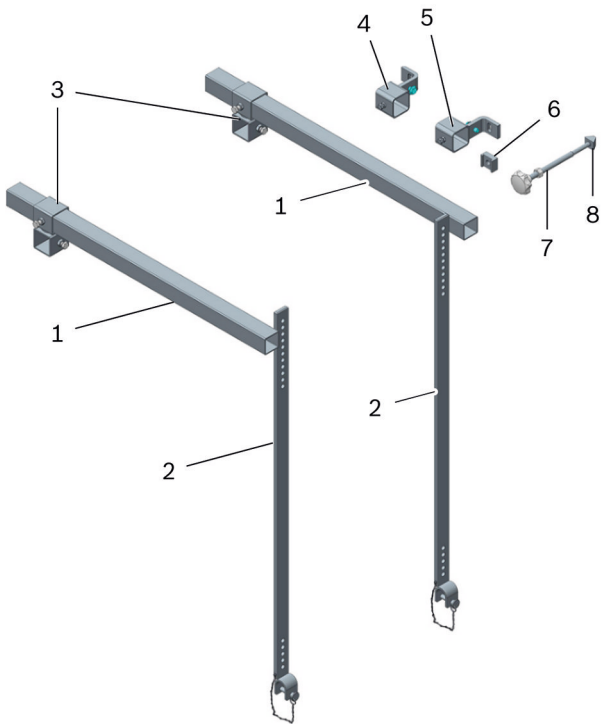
Conjunto básico de dispositivo de soporte de motor T40091
